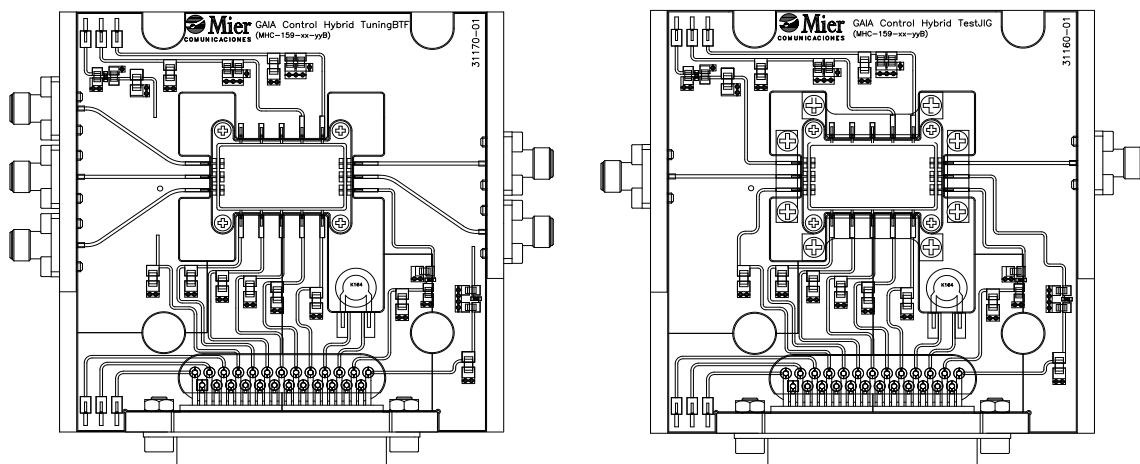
C.H.Tuning Jig (esquerra) i C.H.Test Jig (esquerra).
